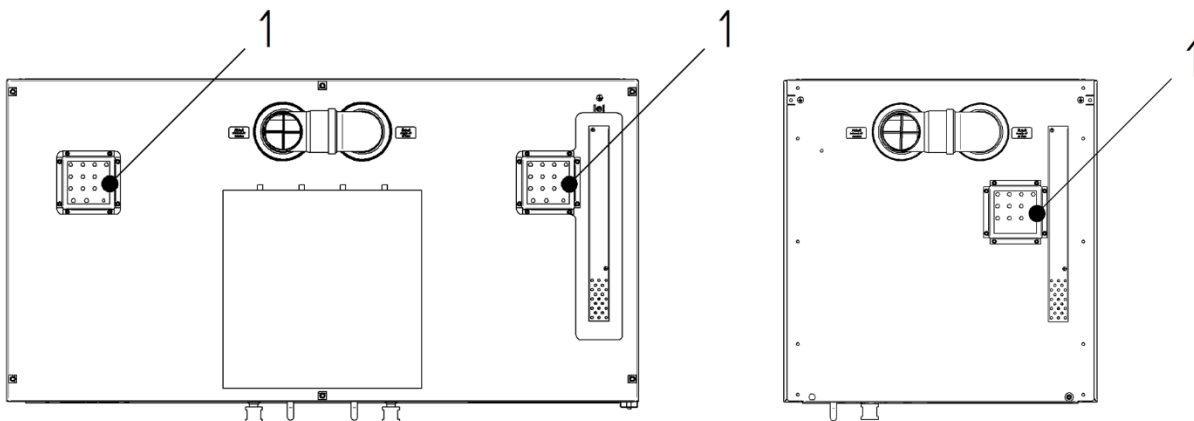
Schrankdach mit Rohrdurchführungen (Links: BATTERY station XL; Rechts: BATTERY standard M)
